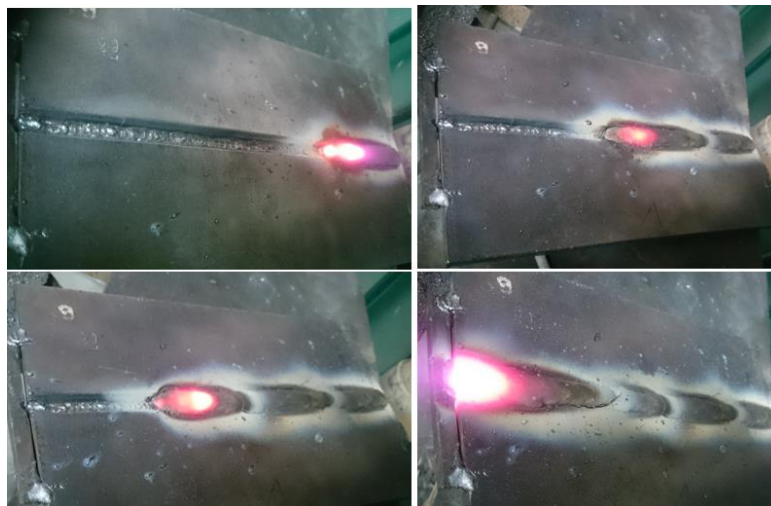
Secuencia de soldadura del cordón de relleno
